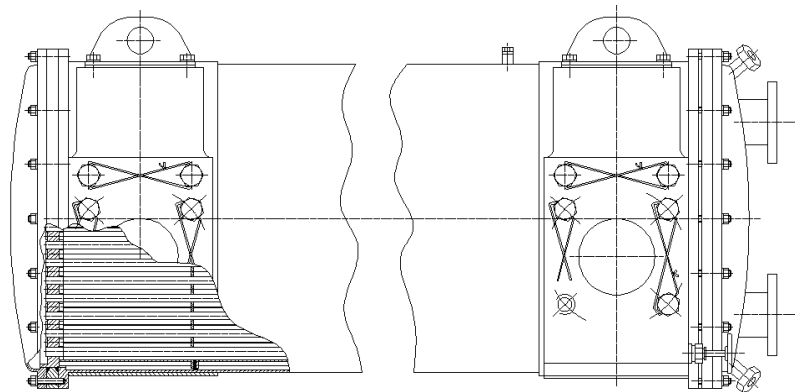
Загальний вид кожухотрубного маслоохолоджувача
